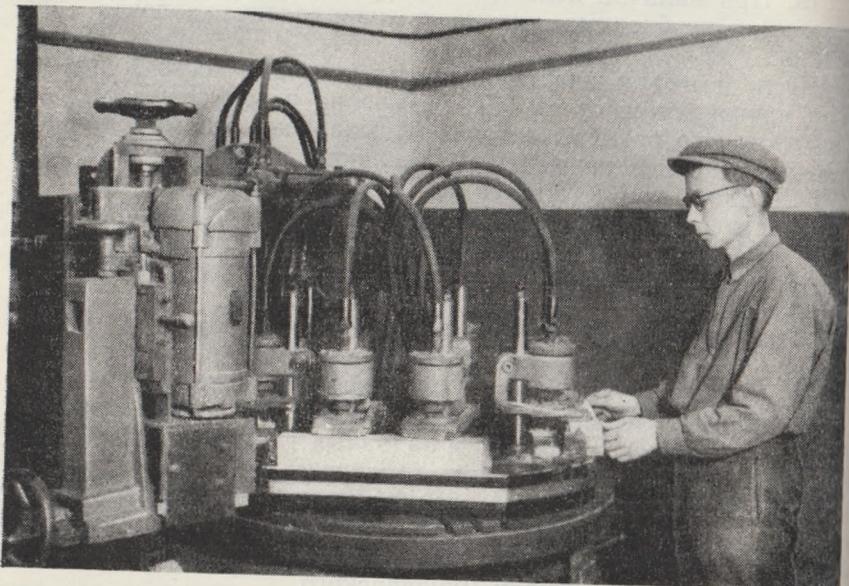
Обработка кромок ручек гитар на карусельно-фрезерном станке
